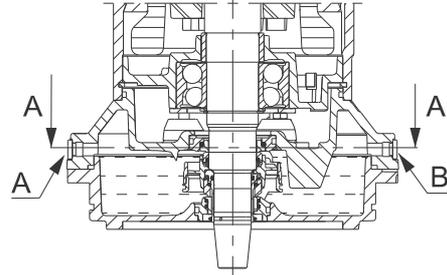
Comprobación del nivel de líquido de motor con la bomba en posición vertical
